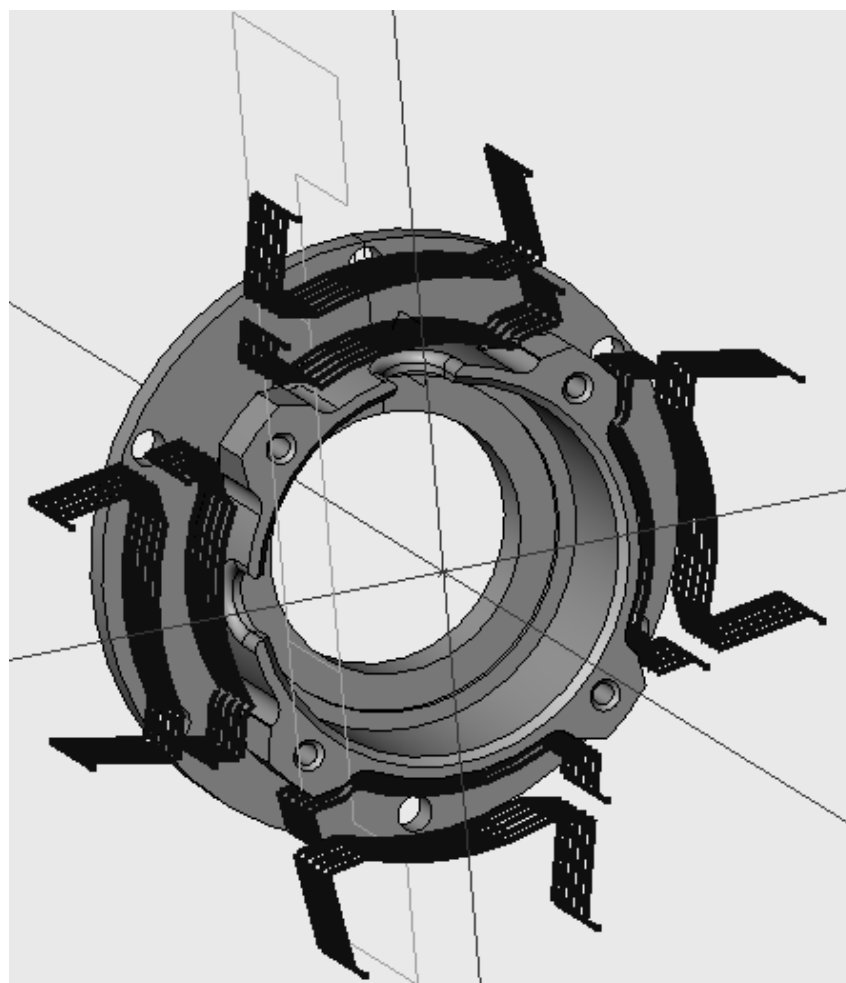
Эквидистанта движения режущего инструмента при обработке сложных пространственных поверхностей «Фланца»
